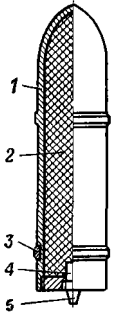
Фугасно-бронейный снаряд с пластическим ВВ: 1 — корпус; 2 — пластическое ВВ; 3 — ведущий пояс; 4 — взрыватель; 5 — трассёр.
